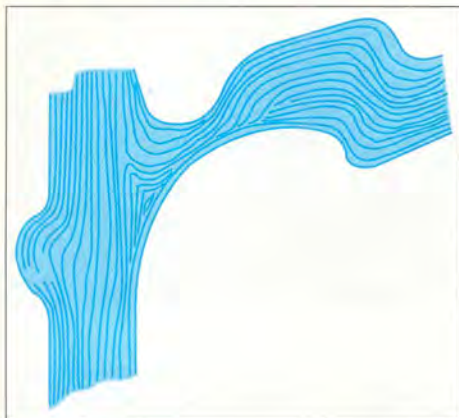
Схема расположения волокон металла после ковки (фрагмент колеса)
